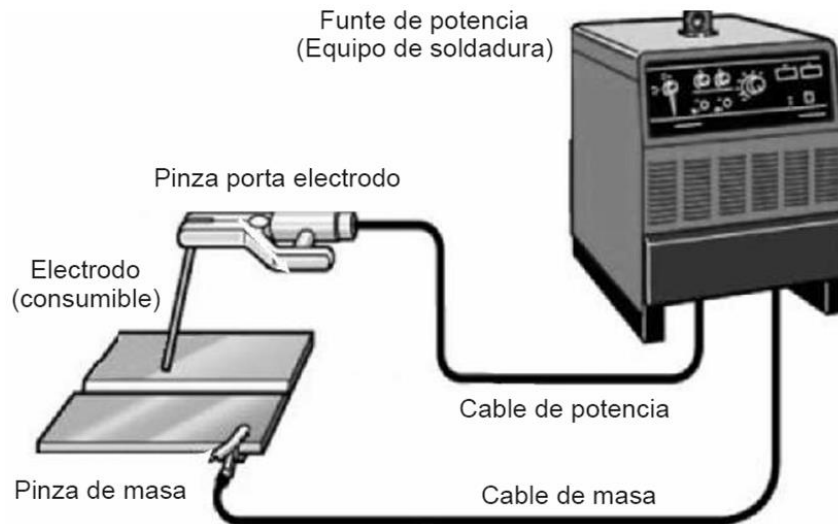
Esquema de equipo de soldadura por arco eléctrico [18].
